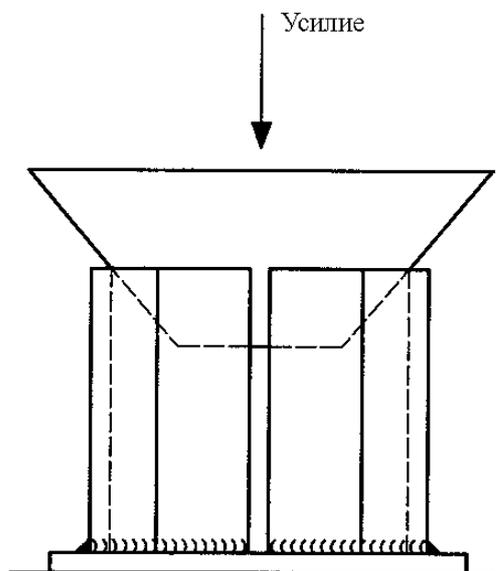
Подготовка и испытание на излом контрольных образцов для угловых швов в трубе
